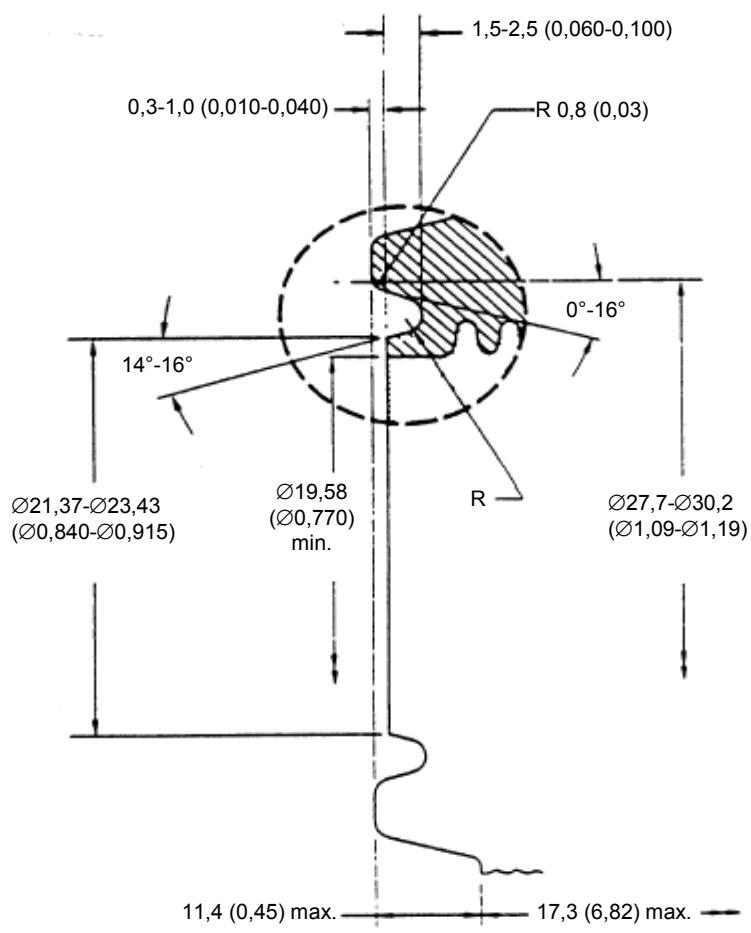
Dimensions des bornes en mm (ref. cône 1/9)
